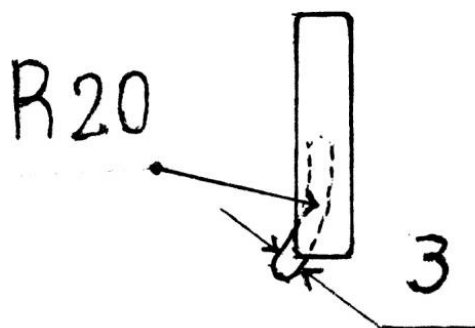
Схема инструмента для малоинвазивной декомпрессии позвоночного канала, вид сзади
